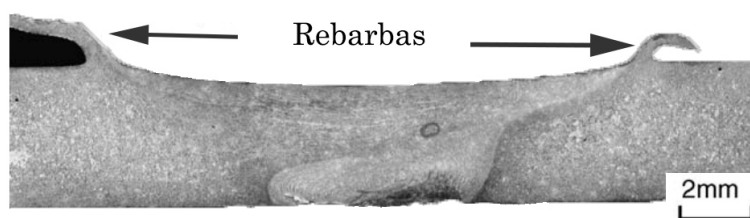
Defeito de rebarba numa soldadura dissimilar por *FSW* [132].
